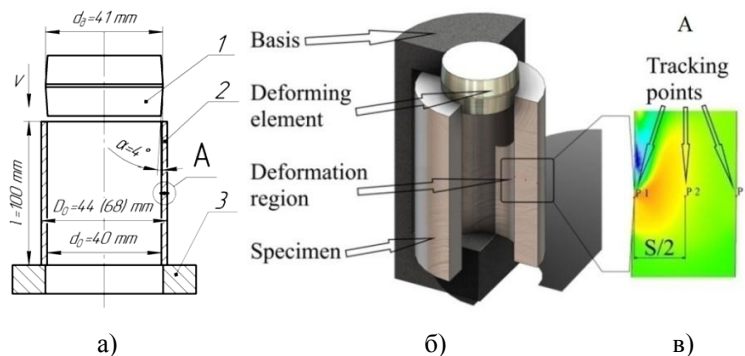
Побудова моделі: а) схема обробки: 1 – деформуючий елемент; 2 – осесиметрична заготовка; 3 – основа; б) моделювання деформуючого протягування; в) графічна картина НДС фрагменту обробленої поверхні
